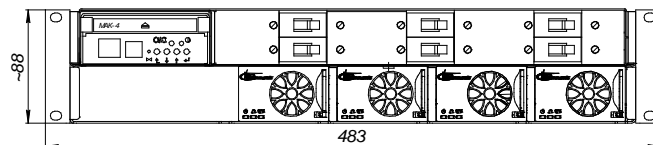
Габаритный чертеж УЭПС-7К 48/148 (60/120)-44-1
